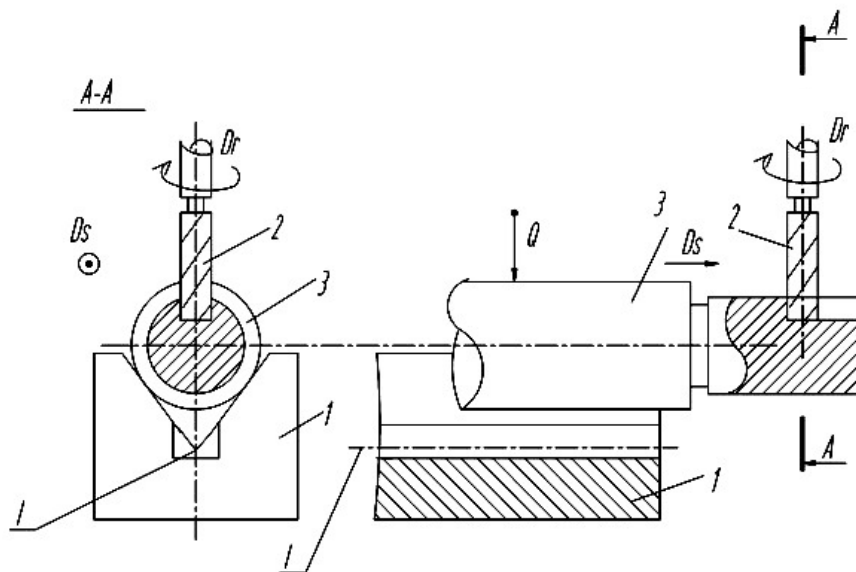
Схема фрезерования шпоночного паза: 1 – технологическая база вала; 1 – призма (элемент приспособления к фрезерному станку); 2 – шпоночная фреза; 3 – заготовка вала со шпоночным пазом;  $D_r$  – главное движение резания;  $D_s$  – движение подачи
